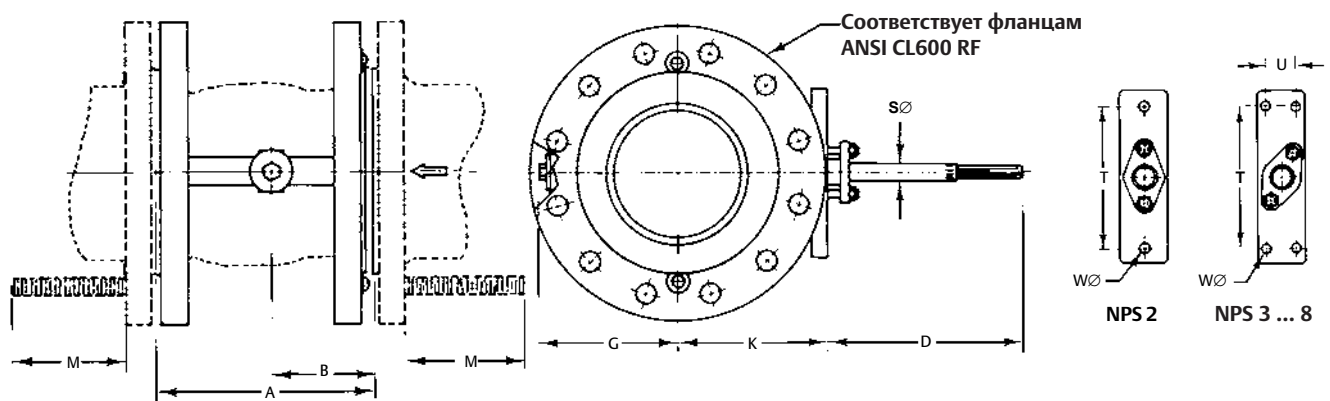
Размеры V200 CL600 фланцевый корпус (см. табл. 7)
